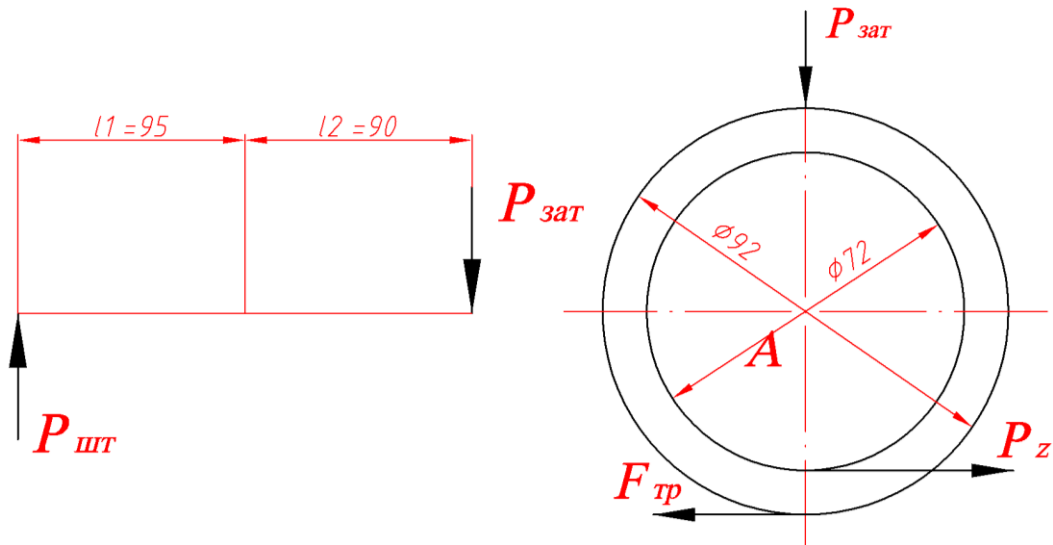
Схема розрахунку зусилля затискування і необхідного діаметра пневмоциліндра
